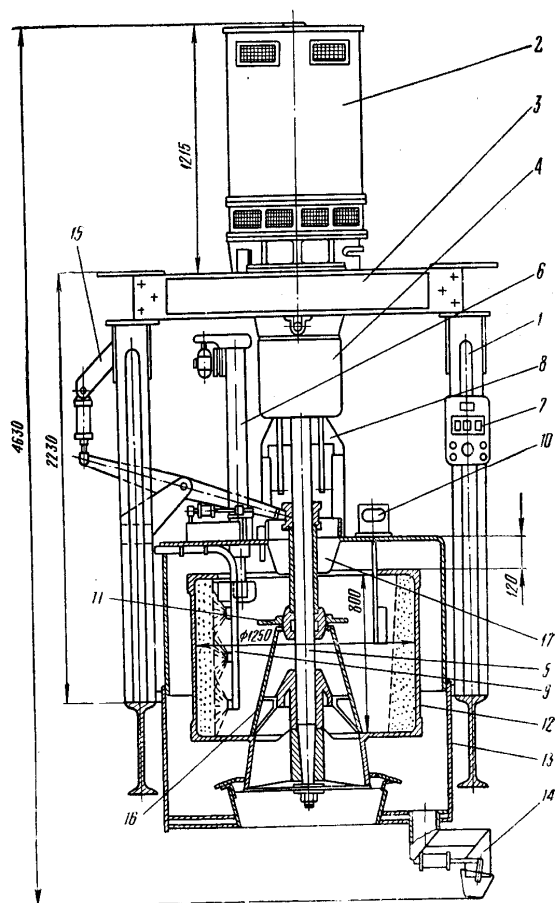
Автоматизированная циклическая центрифуга ФПН-125 1Л - (2)З (АПН –1250) Сумского машиностроительного завода им. Фрунзе : 1 – металлоконструкция; 2 – электродвигатель; 3 – коробка; 4 – привод; 5 – вал; 6 – механический нож выгрузки осадка; 7 – пульт управления; 8 – питатель; 9 – узел промывки; 10 – датчик загрузки; 11 – диск распределительный; 12 – ротор; 13 – кожух; 14 – сегрегатор; 15 – поддон; 16 – конус; 17 – лоток
